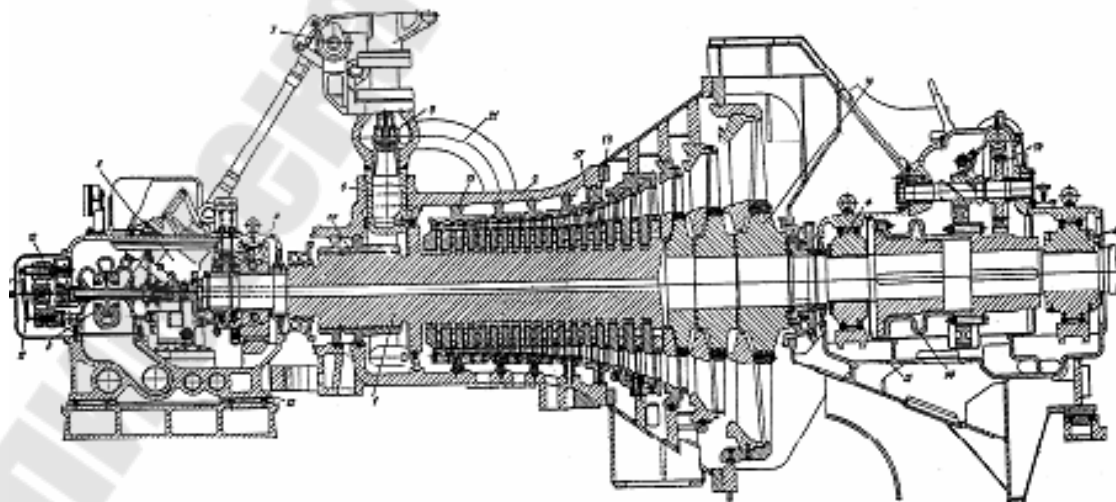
Продольный разрез турбины К-50-90: 1 – ротор турбины; 2 – корпус турбины; 3 – опорно-упорный подшипник; 4 – опорный подшипник; 5 – регулирующий лапан; 6 – сопловая коробка; 7 –
